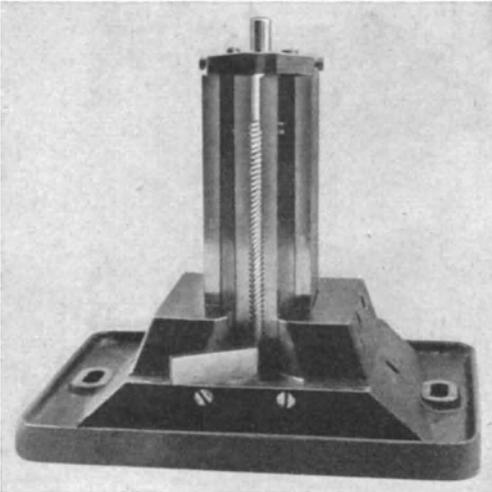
Gebautes Räumzeug zur beiderseitigen Bearbeitung eines Werkstückes (Schilling).
